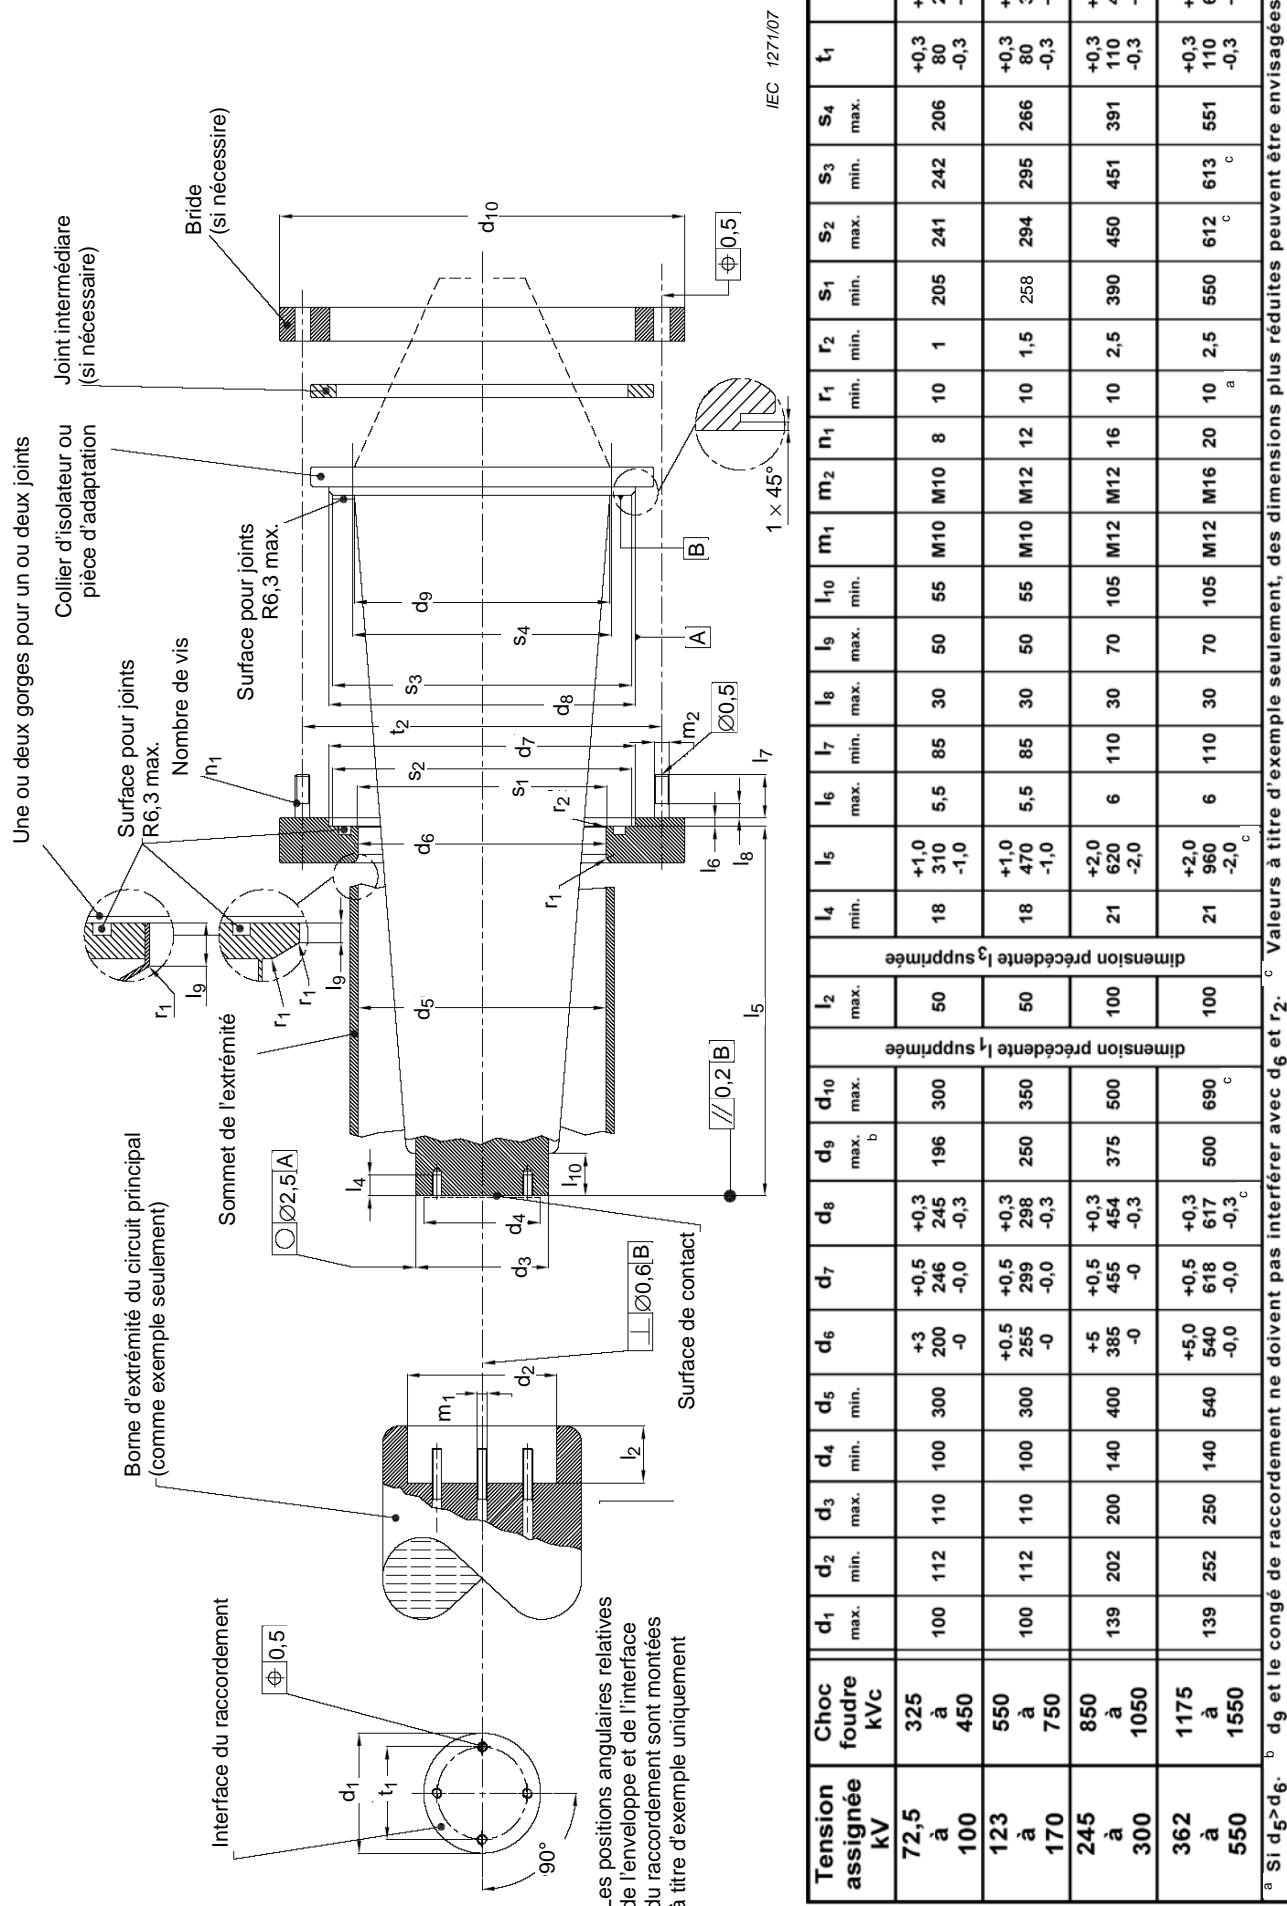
Assemblage de raccordement de câble sec – Dimensions
